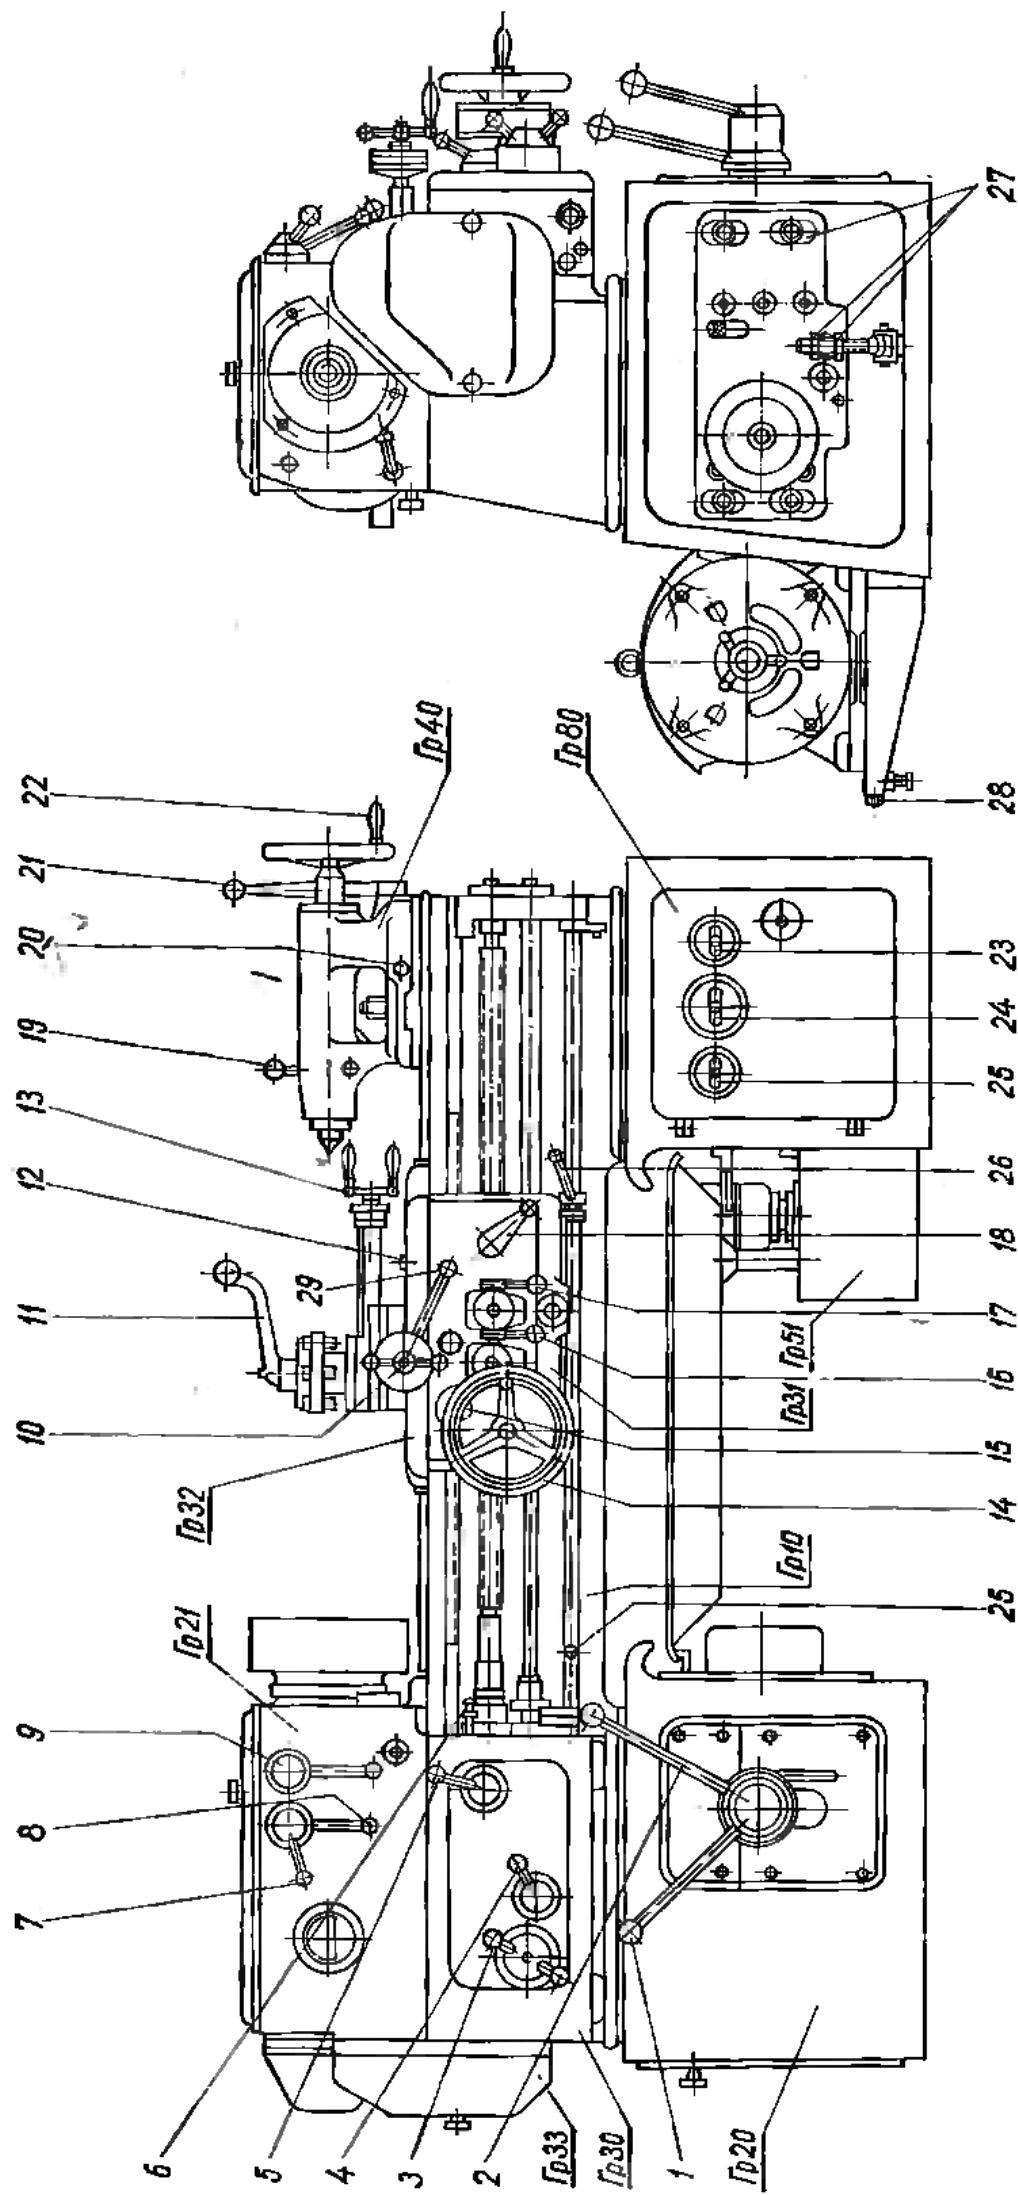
Органы управления станка: 1, 2 — рукоятка управления коробки скоростей; 3, 4, 5 — рукоятки установки величины подачи и шага резьбы; 6 — рукоятка переключения ходового валика и ходового винта; 7 — рукоятка включения нормального и увеличенного шага; 8 — рукоятка изменения направления подачи; 9 — рукоятка включения перебора; 10 — рукоятка поперечной подачи суппорта; 11 — рукоятка поворота и крепления головки; 12 — винт крепления каретки к станине; 13 — рукоятка подачи верхней части суппорта; 14 — маховичек ручного перемещения каретки; 15 — кнопка выключения реечной шестерни из рейки при нарезании резьбы; 16 — рукоятка включения продольной подачи суппорта; 17 — рукоятка включения поперечной подачи суппорта; 18 — рукоятка включения гайки ходового винта; 19 — рукоятка крепления задней бабки к станине; 20 — винт поперечного смещения пинноли задней бабки; 21 — рукоятка крепления насоса охлаждения; 24 — рукоятка включения электрооборудования станка в сеть; 25 — рукоятка включения местного освещения; 26 — рукоятки (2) пуска станка и резервирования шпинделя; 27 — винты натяжения ремней шпиндельной бабки; 28 — винты натяжения ремней электродвигателя; 29 — рукоятка быстрого отвода резца
